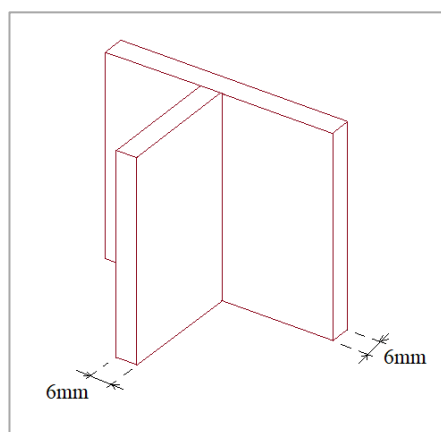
Junta de soldadura de canto (fonte: West-sea)
